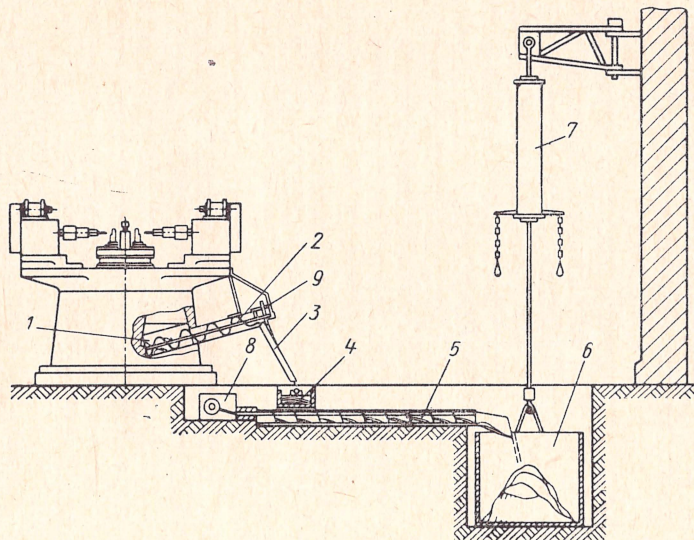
Схема механизированной уборки стружки с участка агрегатных станков
